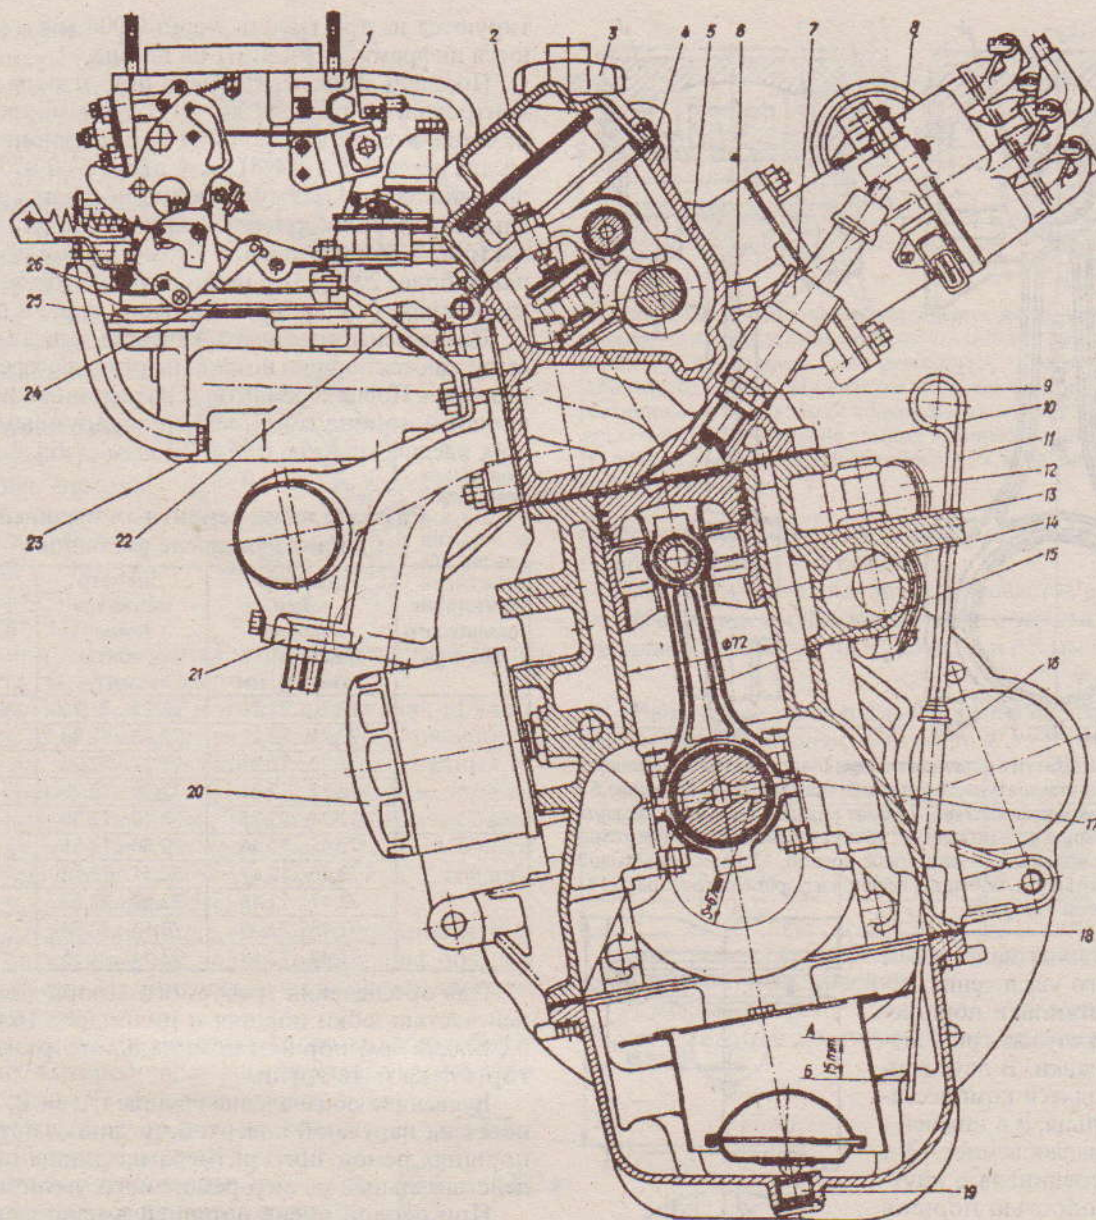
Поперечный разрез двигателя: 1 - карбюратор; 2 - крышка головки цилиндров; 3 - крышка маслозаливной горловины; 4 - прокладка крышки головки цилиндров; 5 - головка цилиндров; 6 - болт крепления головки цилиндров; 7 - наконечник свечи; 8 - датчик-распределитель; 9 - свеча зажигания; 10 - прокладка головки цилиндров; 11 - маслоизмерительный стержень; 12 - трубка, подводящая жидкость; 13 - палец поршня; 14 - поршень; 15 - шатун; 16 - трубка маслоизмерительного стержня; 17 - коленчатый вал; 18 - прокладка масляного картера; 19 - маслозаливная пробка; 20 - масляный фильтр; 21 - выпускной коллектор; 22 - рым-планка; 23 - впускной коллектор; 24 - проставка фланца; 25 - топливоборник; 26 - прокладка фланца карбюратора. Уровни масла: А - верхний, равный 3,45 л и Б-нижний, равный 2,45 л
